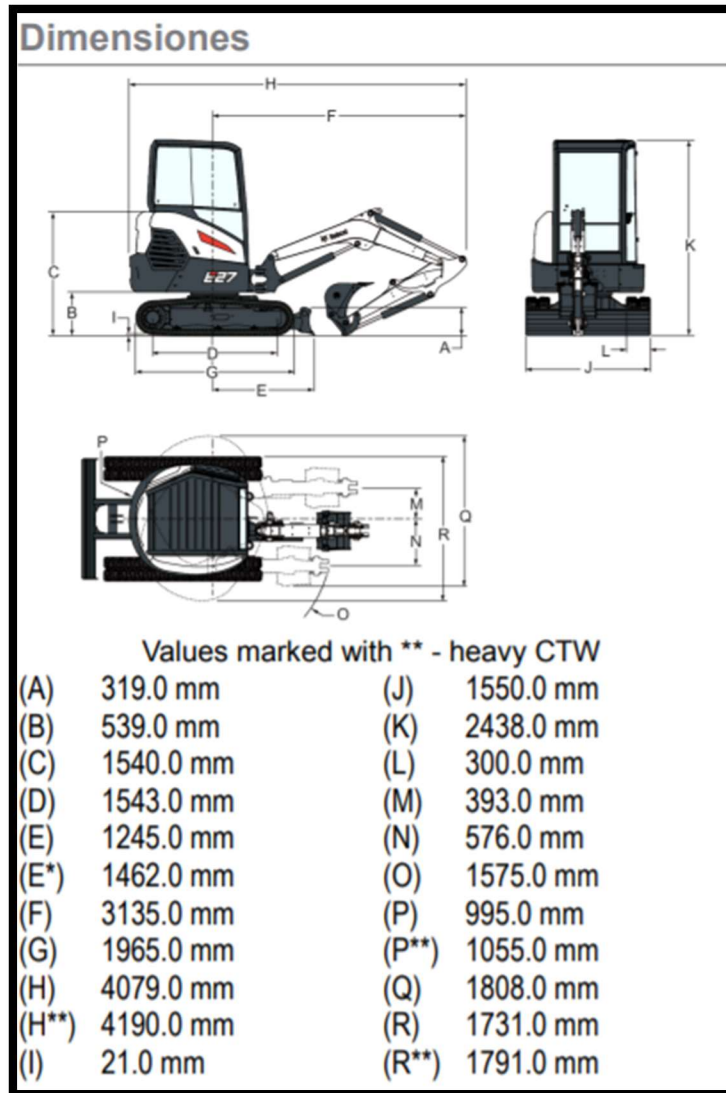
Dimensiones Retroexcavadora Compactadora – Fuente: Bobcat.com
